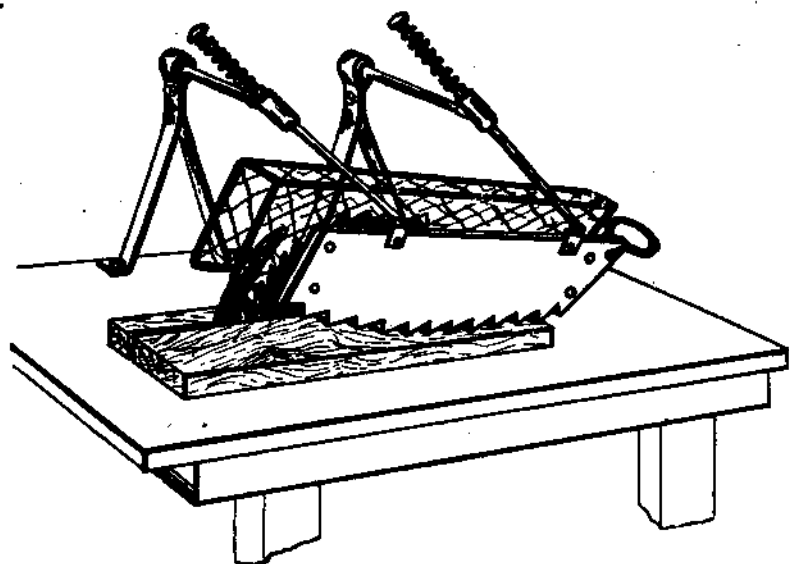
Направляющий прибор для круглой пилы фирмы Aublet, Harry & Co.
